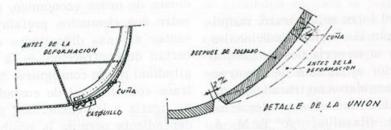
Preparación de la soldadura del pantoque.
